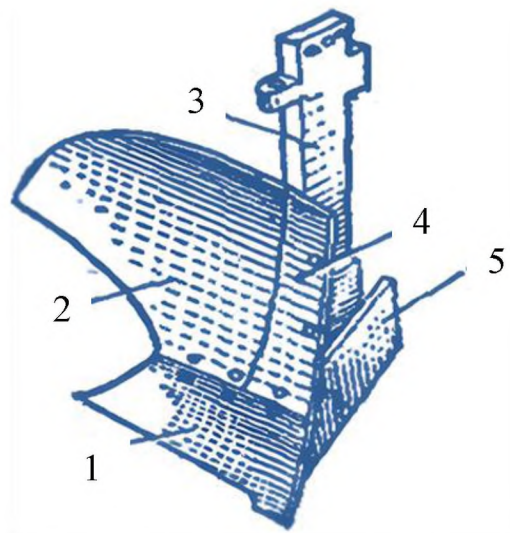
Корпус плуга: 1 - леміш; 2 - полиця; 3 - стійка; 4 - вставка;
